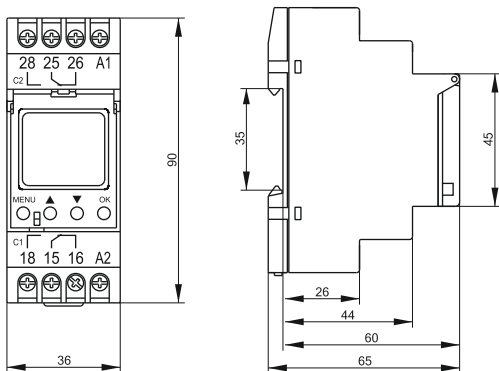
Рисунок / figure 2 – Габаритные и установочные размеры / Overall and mounting dimensions
